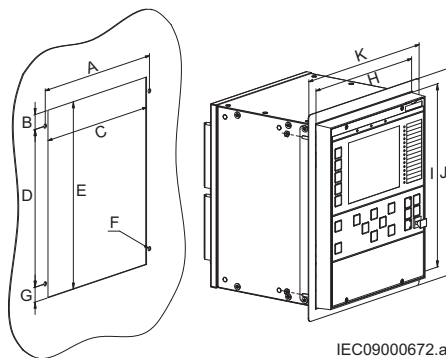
Einbau des Gerätes in einen Plattenausschnitt
